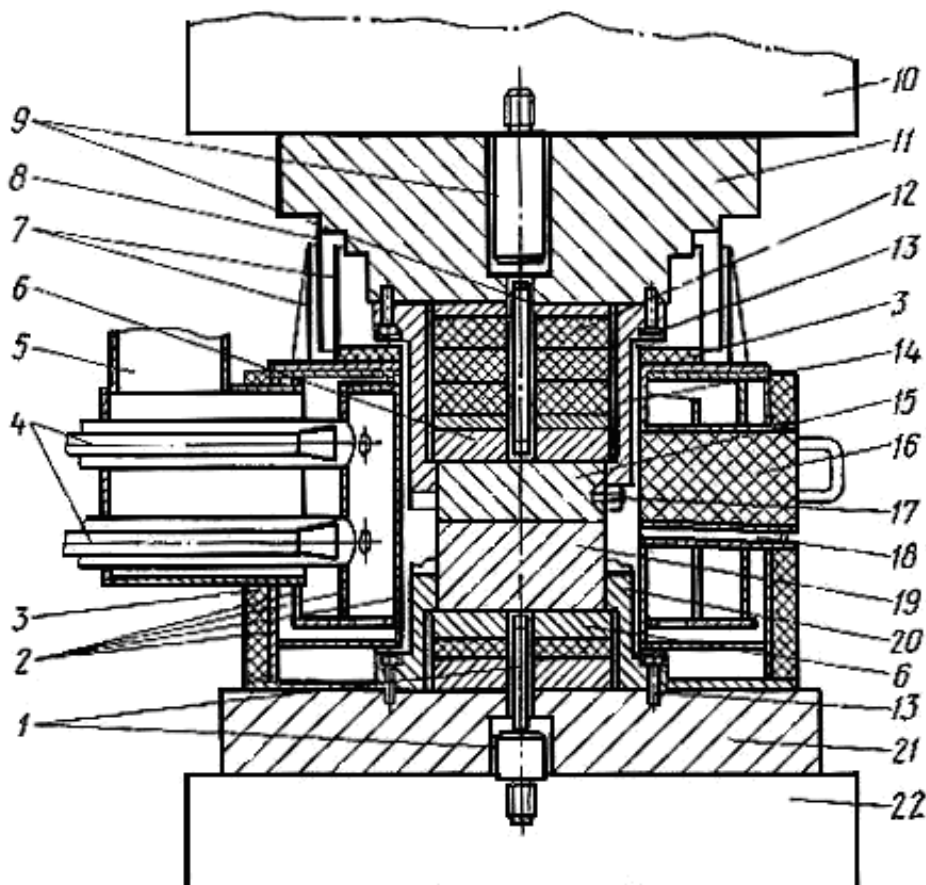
Штампный блок для изотермического деформирования металлов с газовым нагревом заготовок
